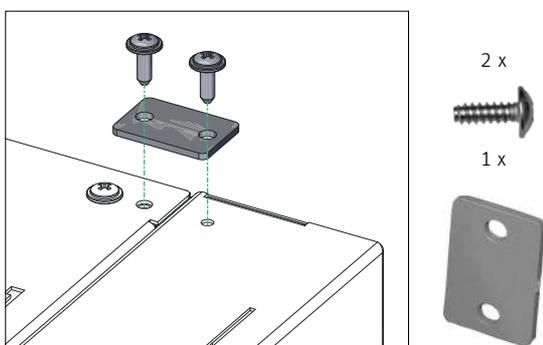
Avvitare la parete laterale in alto e la piastrina di fissaggio con 2 viti autofilettanti
